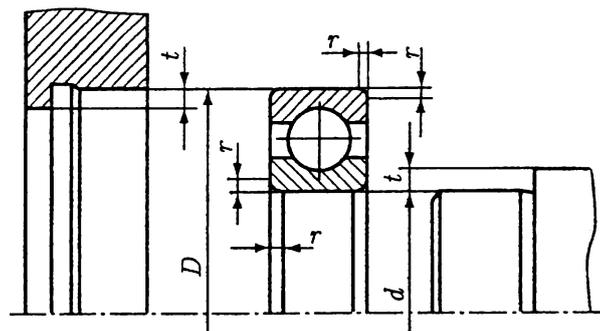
Буртики (заплечики) на валу и в отверстии корпуса для упора колец подшипников
